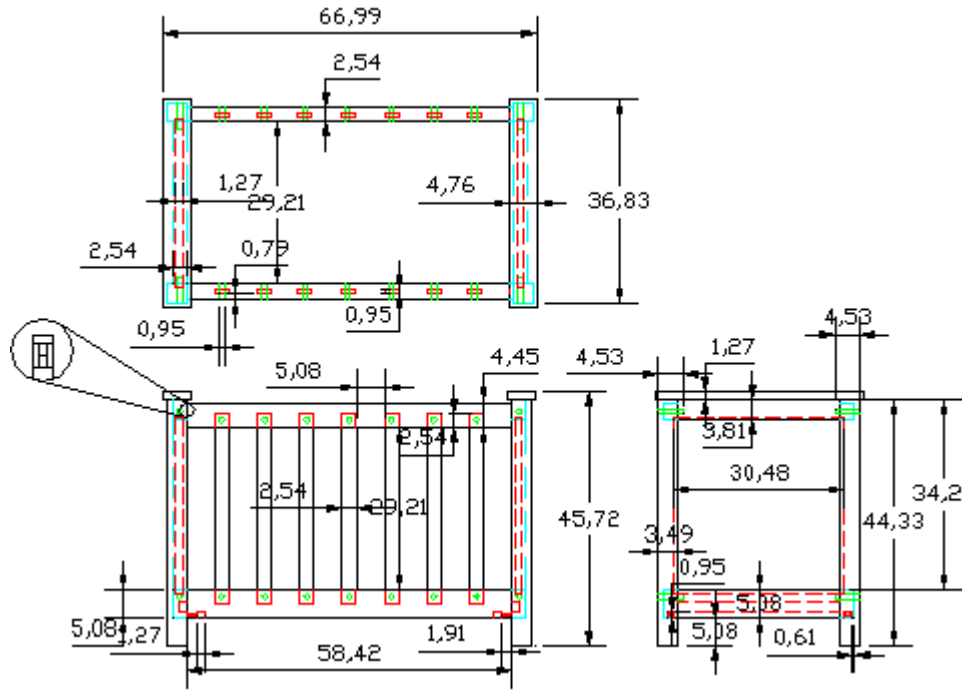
Plan de conception illustrant les trois vues principales du lit pour bébé conçu selon la technique d'assemblage par soudage rotationnel.
